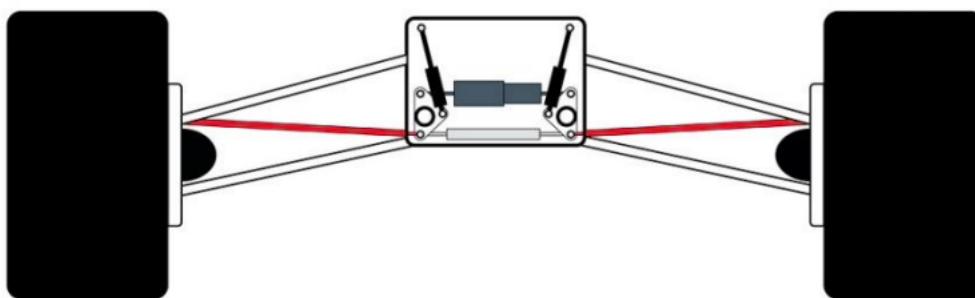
Кінематична схема підвіски типу Push Rod
